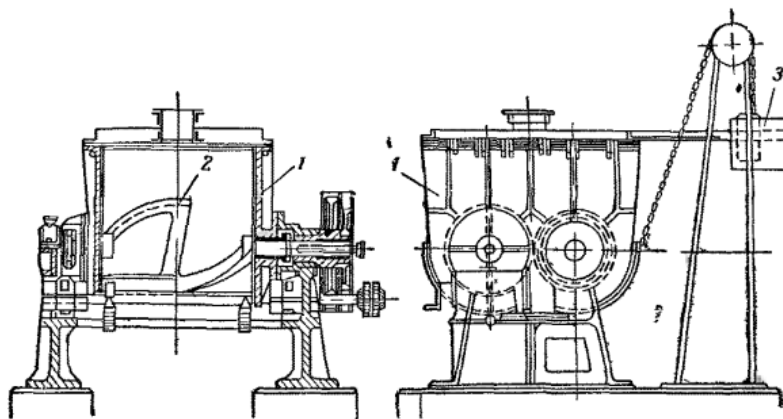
Двовальний змішувач з фасонними лопатями:
